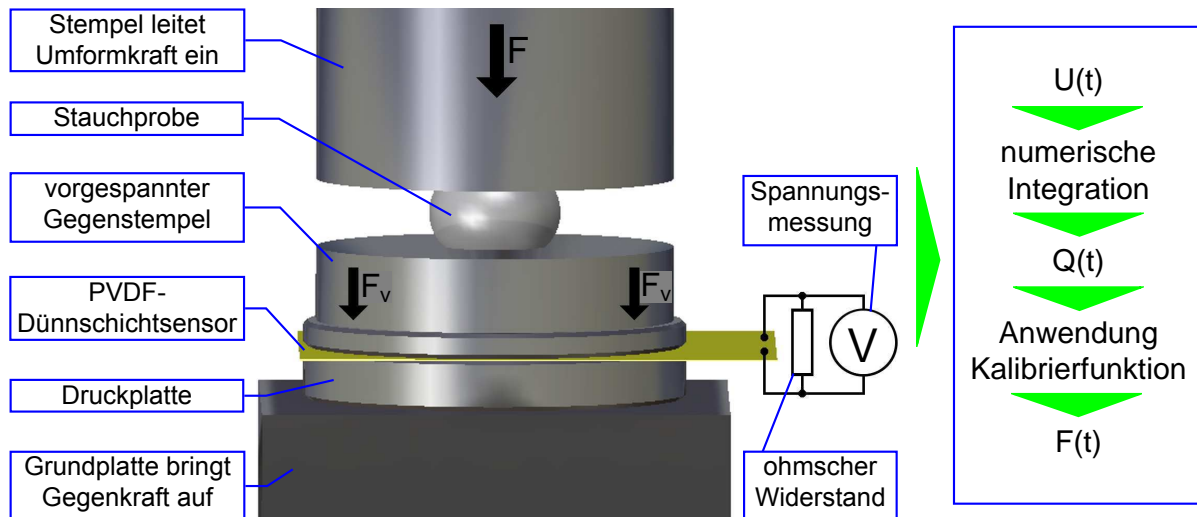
Konzept werkzeugintegrierter Kraftmessung
